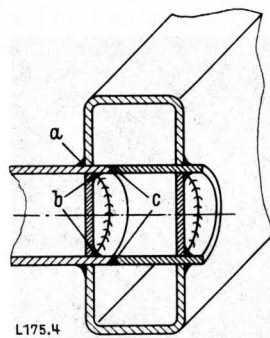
Ausführung für durchgehenden Querträger mit im Bereich des Kastenprofils verschweißtem Rohr.
